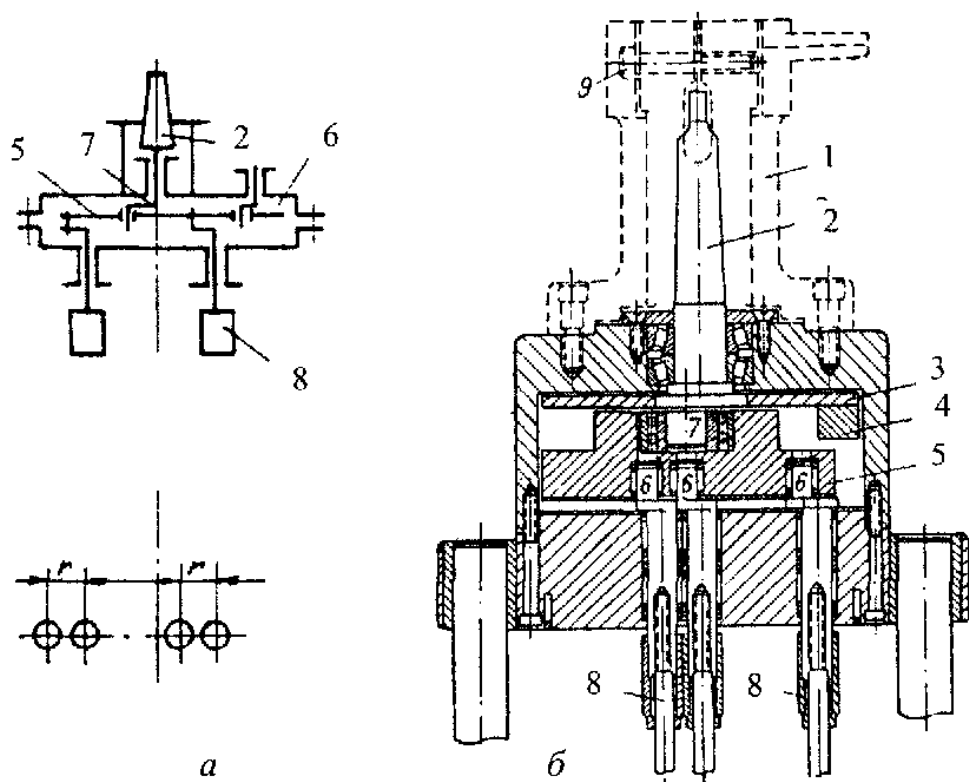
Схема багатошпindelної кривошипно-шатуної свердильної головки з постійним розташуванням шпindelів
